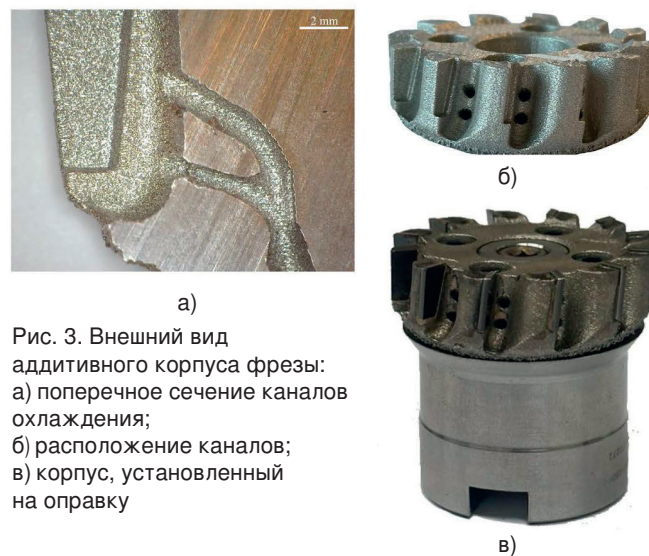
Внешний вид аддитивного корпуса фрезы:
